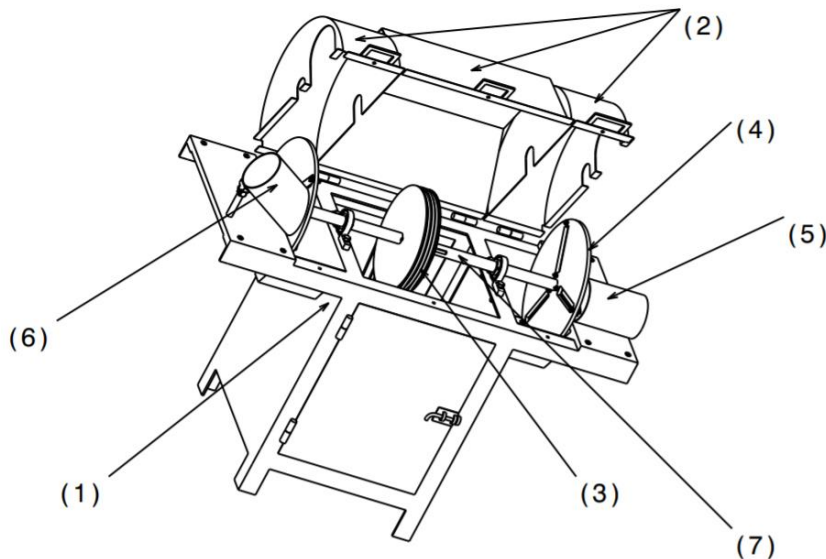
Dessin d'ensemble de la découpeuse réalisé sur CATIA V5R20
